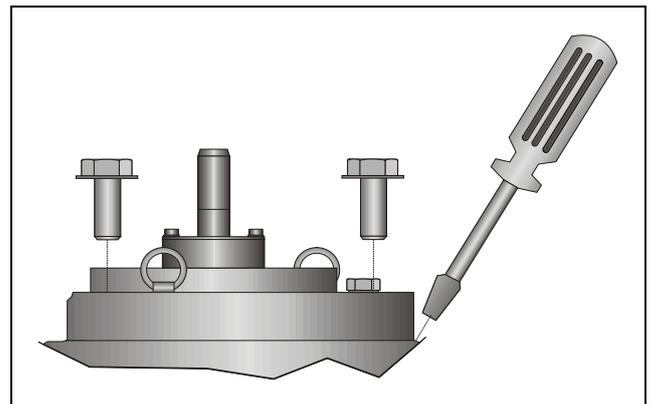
Desserrage et retrait des vis à six pans au niveau du couvercle de filtre
